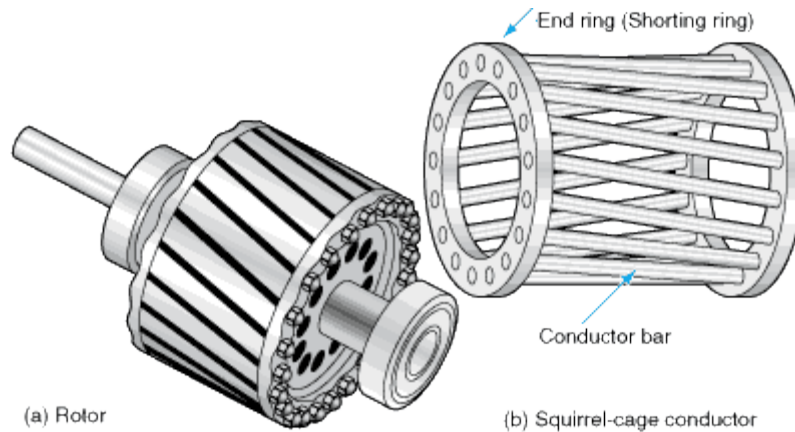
Le rotor à cage d'écureuil du moteur asynchrone.
